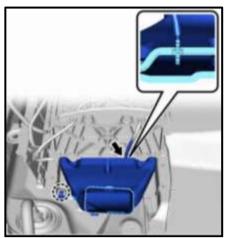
Desmontaje del conjunto de bloque de unión de la batería HV Toyota
